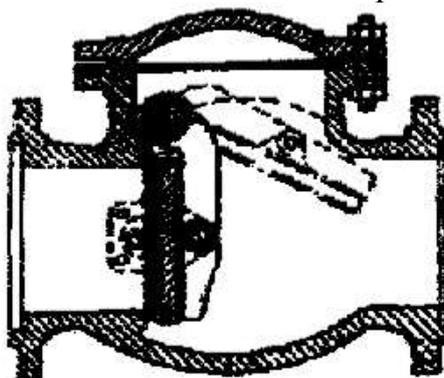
Поворотный обратный клапан D_y 50–600 мм
